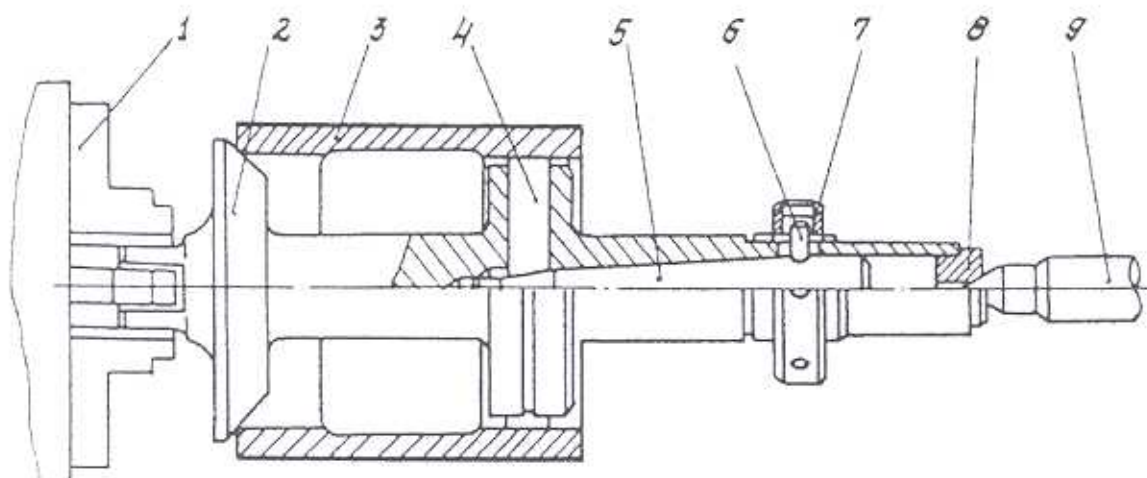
Приспособление для проточки изоляции втулки контактных колец: 1 – патрон токарного станка, 2, 5, 9 – конусы, 3 – втулка контактных колец, 4 – плунжеры, 6 – палец, 7 – гайка, 8 – втулка
